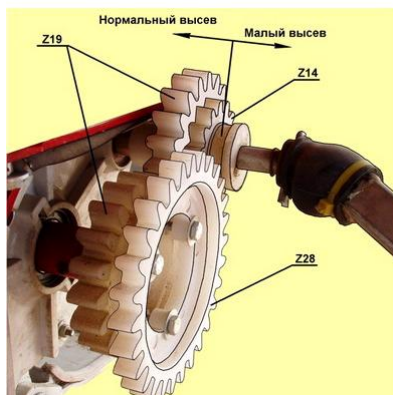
Зубчатый редуктор механизма привода высевающего аппарата
